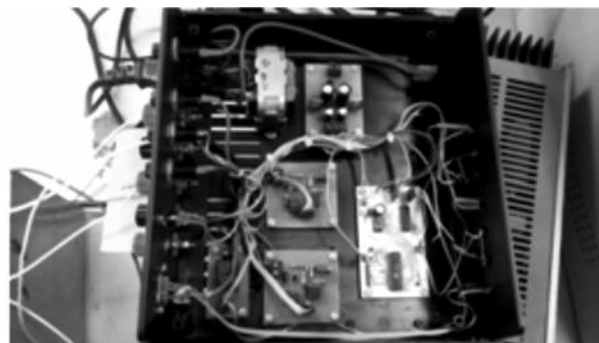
Розташування плат та деталей в корпусі розробленого ПКВ
